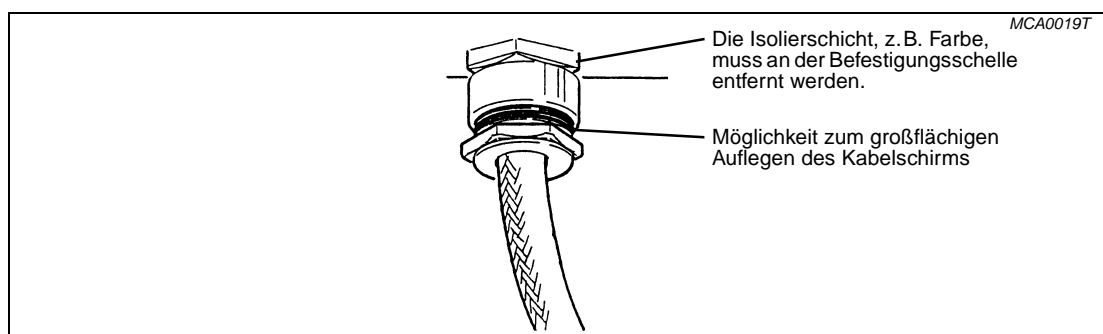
Kabelzuführung mittels metallischer Kabelverschraubung
